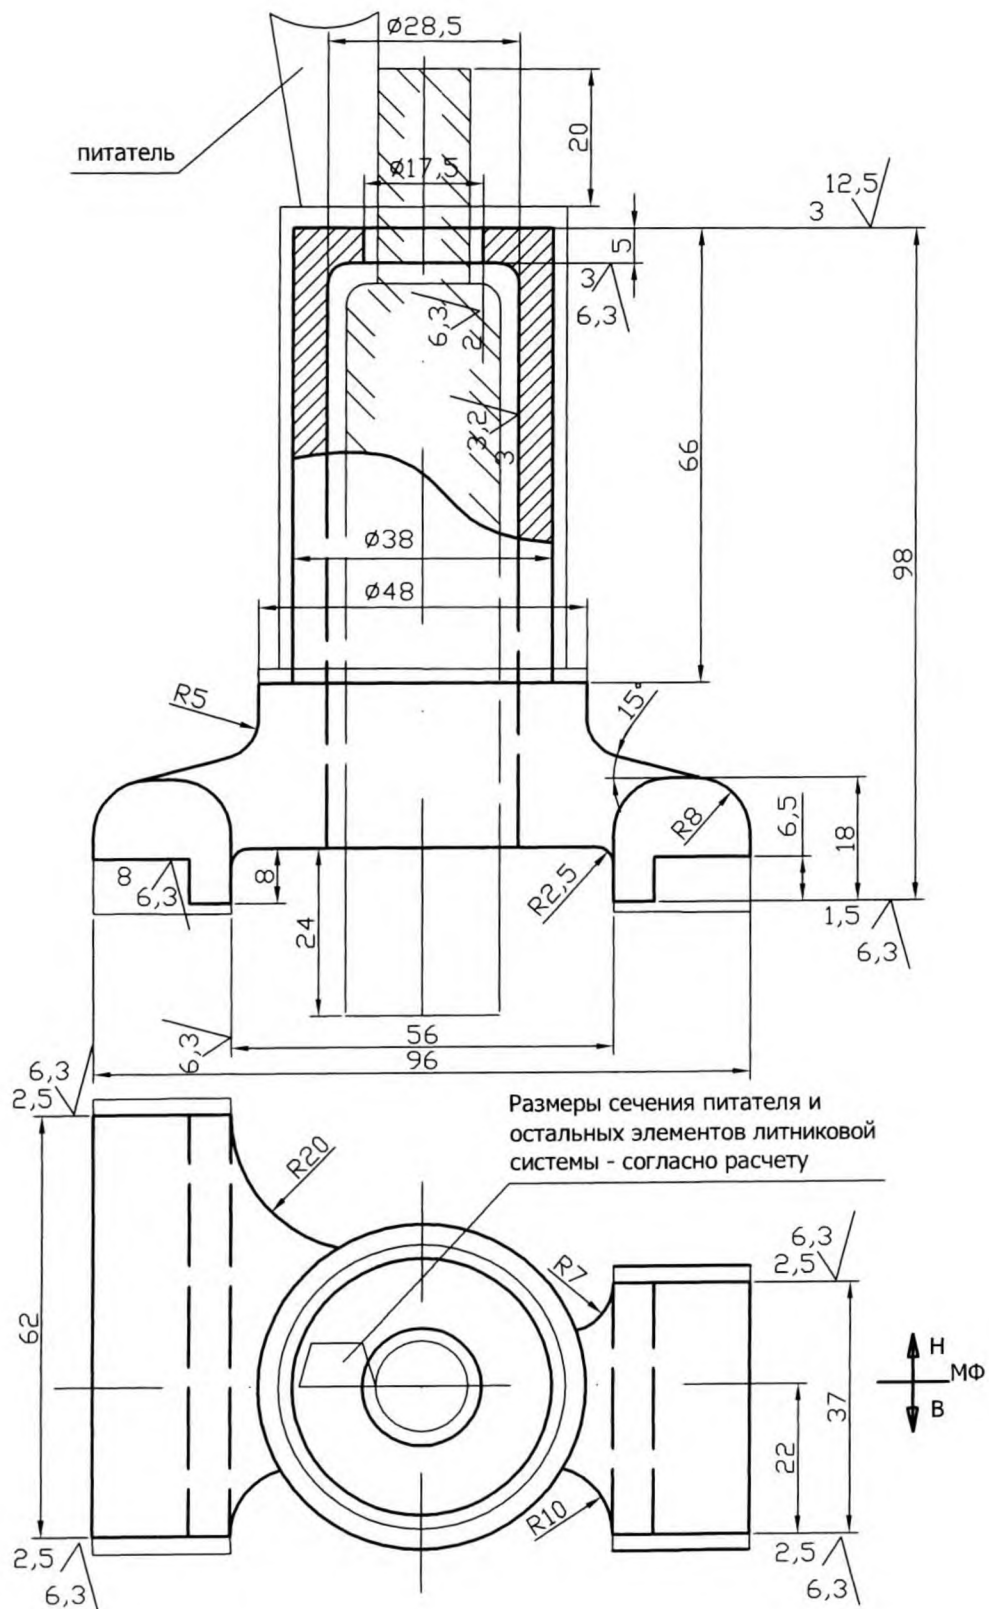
Суппорт. Отливка с элементами литейной формы
